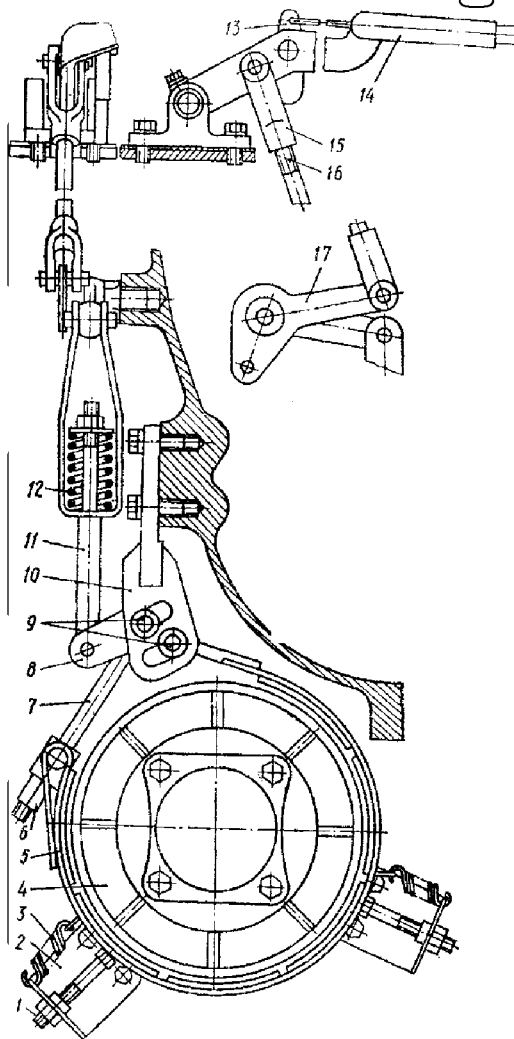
Центральне гальмо (ХТЗ-17221): 1 - регулювальний болт; 2 - кронштейни регулювального болта; 3 - відтяжна пружина; 4 - барабан; 5 - гальмівна стрічка; 6 - регулювальна гайка тяги; 7 - тяга регулювальна стрічки; 8 - важіль тяги компенсуючої пружини; 9 - пальці; 10 - кронштейн стрічки; 11 - тяга компенсуючої пружини; 12 - пружина, що компенсує; 13 - клімка; 14 - важіль управління гальмом; 15 - вилка тяги; 16 - тяга важеля управління; 17 - двоплечий важіль.
